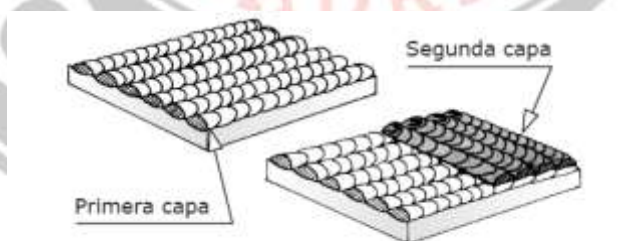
Etapas de relleno o reconstrucción con soldadura por arco
